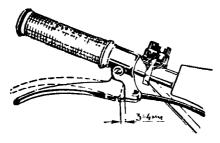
Свободный ход рычага переднего (ручного) тормоза.
